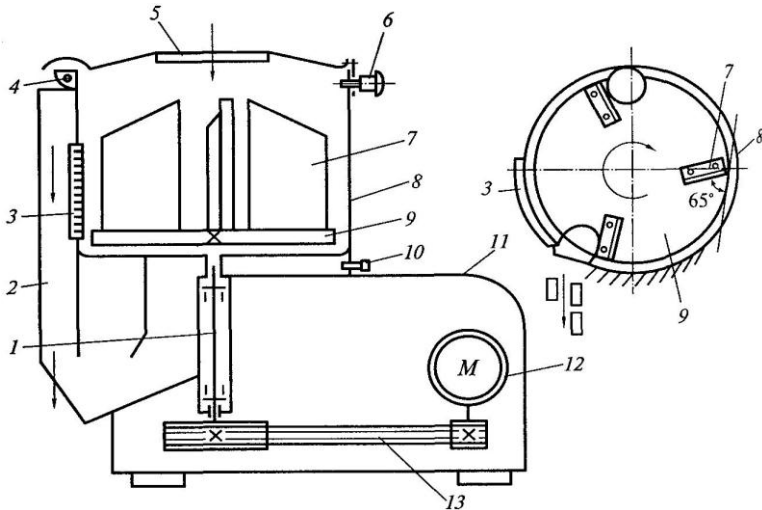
Принципиальная схема роторной овощерезательной машины МРО 400-1000: 1 – выходной вал; 2 – разгрузочный канал; 3 – ножевой блок; 4 – ось; 5 – загрузочная воронка; 6 – фиксатор; 7 – лопасти; 8 – рабочая камера; 9 – диск; 10 – защелка; 11 – корпус; 12 – электродвигатель; 13 – клиноременная передача
